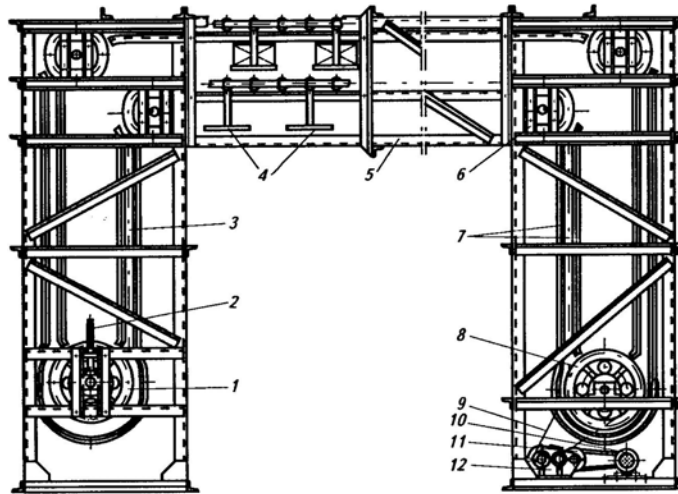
Конструкція дволанцюгового люлечного конвеєра: 1 – натяжна зірочка; 2 – натяжний пристрій; 3 – втулково-катковий ланцюг; 4 – люльки; 5 – металева рама; 6 – поворотна зірочка; 7 – напрямні; 8 – привідна зірочка; 9 – ланцюгова передача; 10 – електричний двигун; 11 – пасова передача; 12 – циліндричний редуктор
